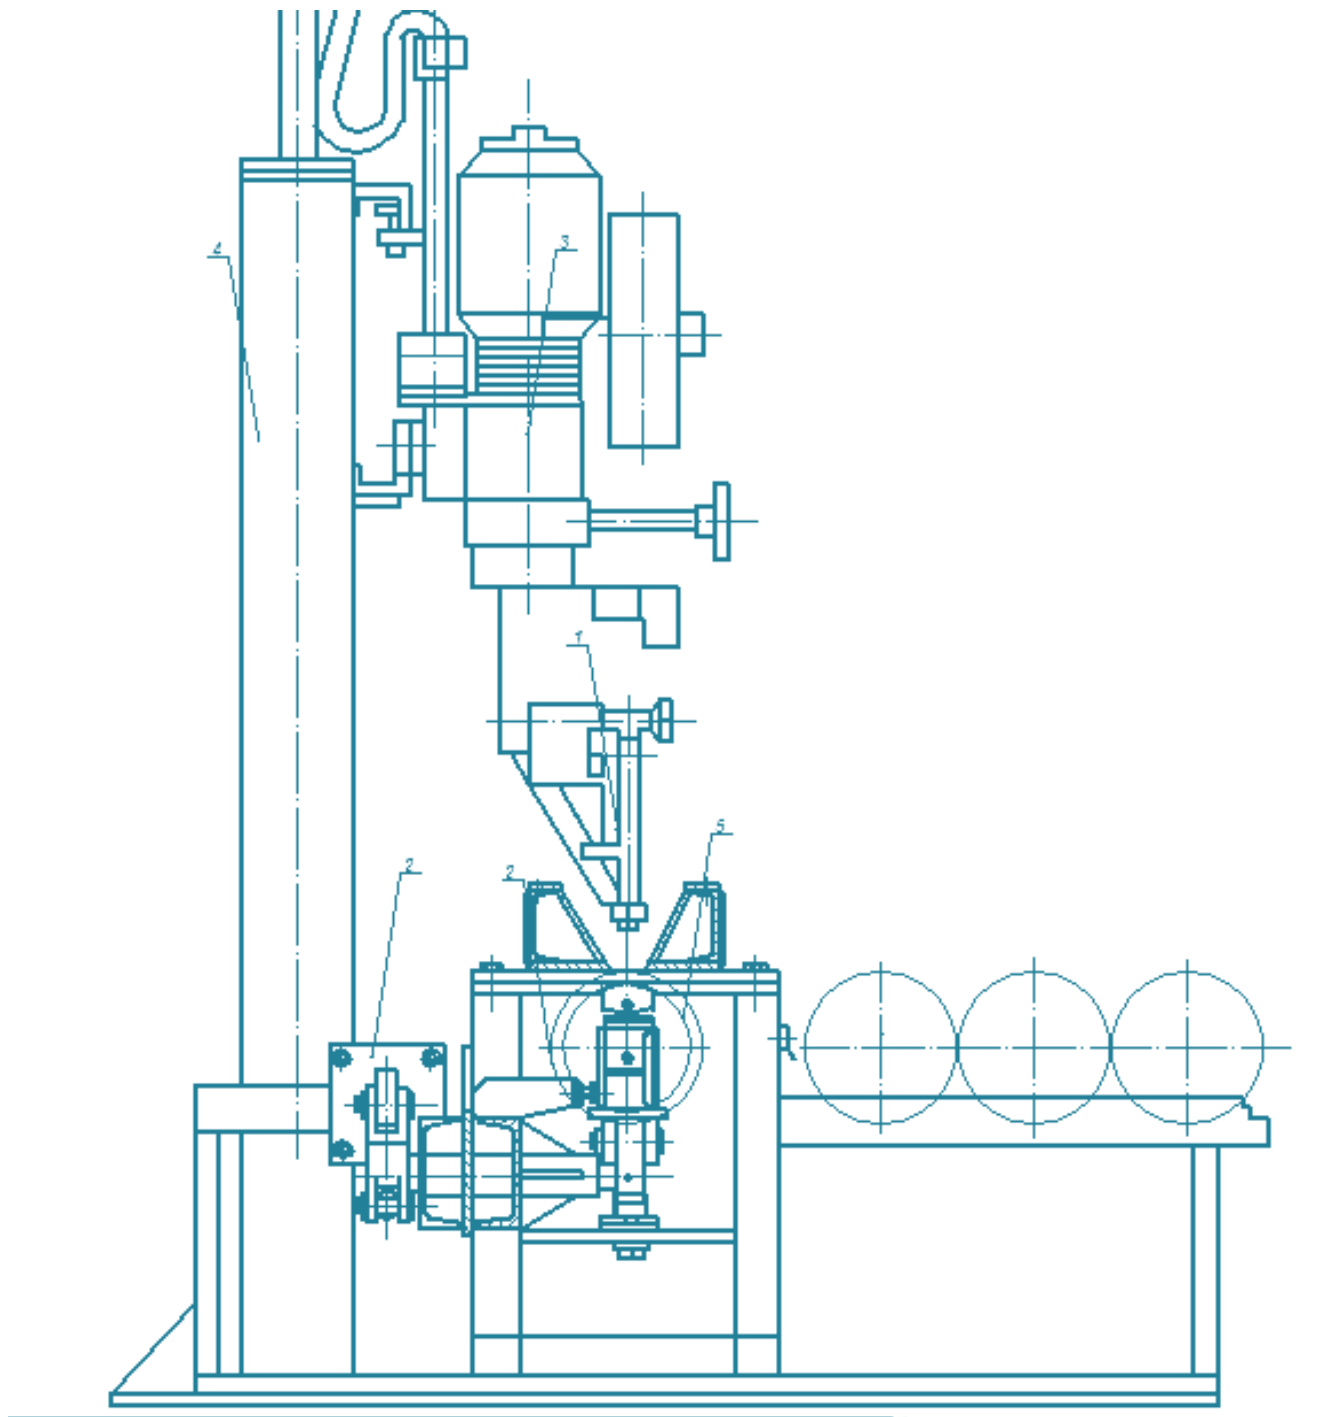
Спеціалізована установка Р-879 на позиції зварювання обичайки
